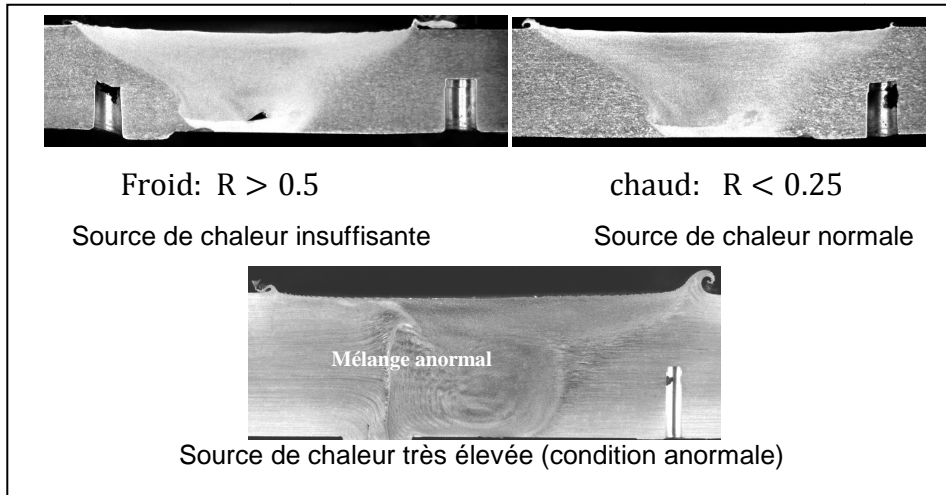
Illustration des conditions de soudage. Cas du soudage de l'aluminium AA7020-T6 (IS).
